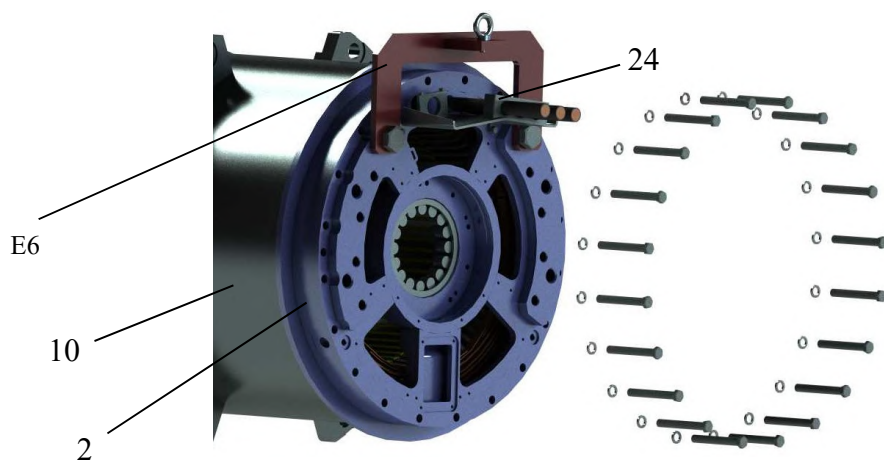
а – Демонтаж подшипникового щита (сторона тормоза)
